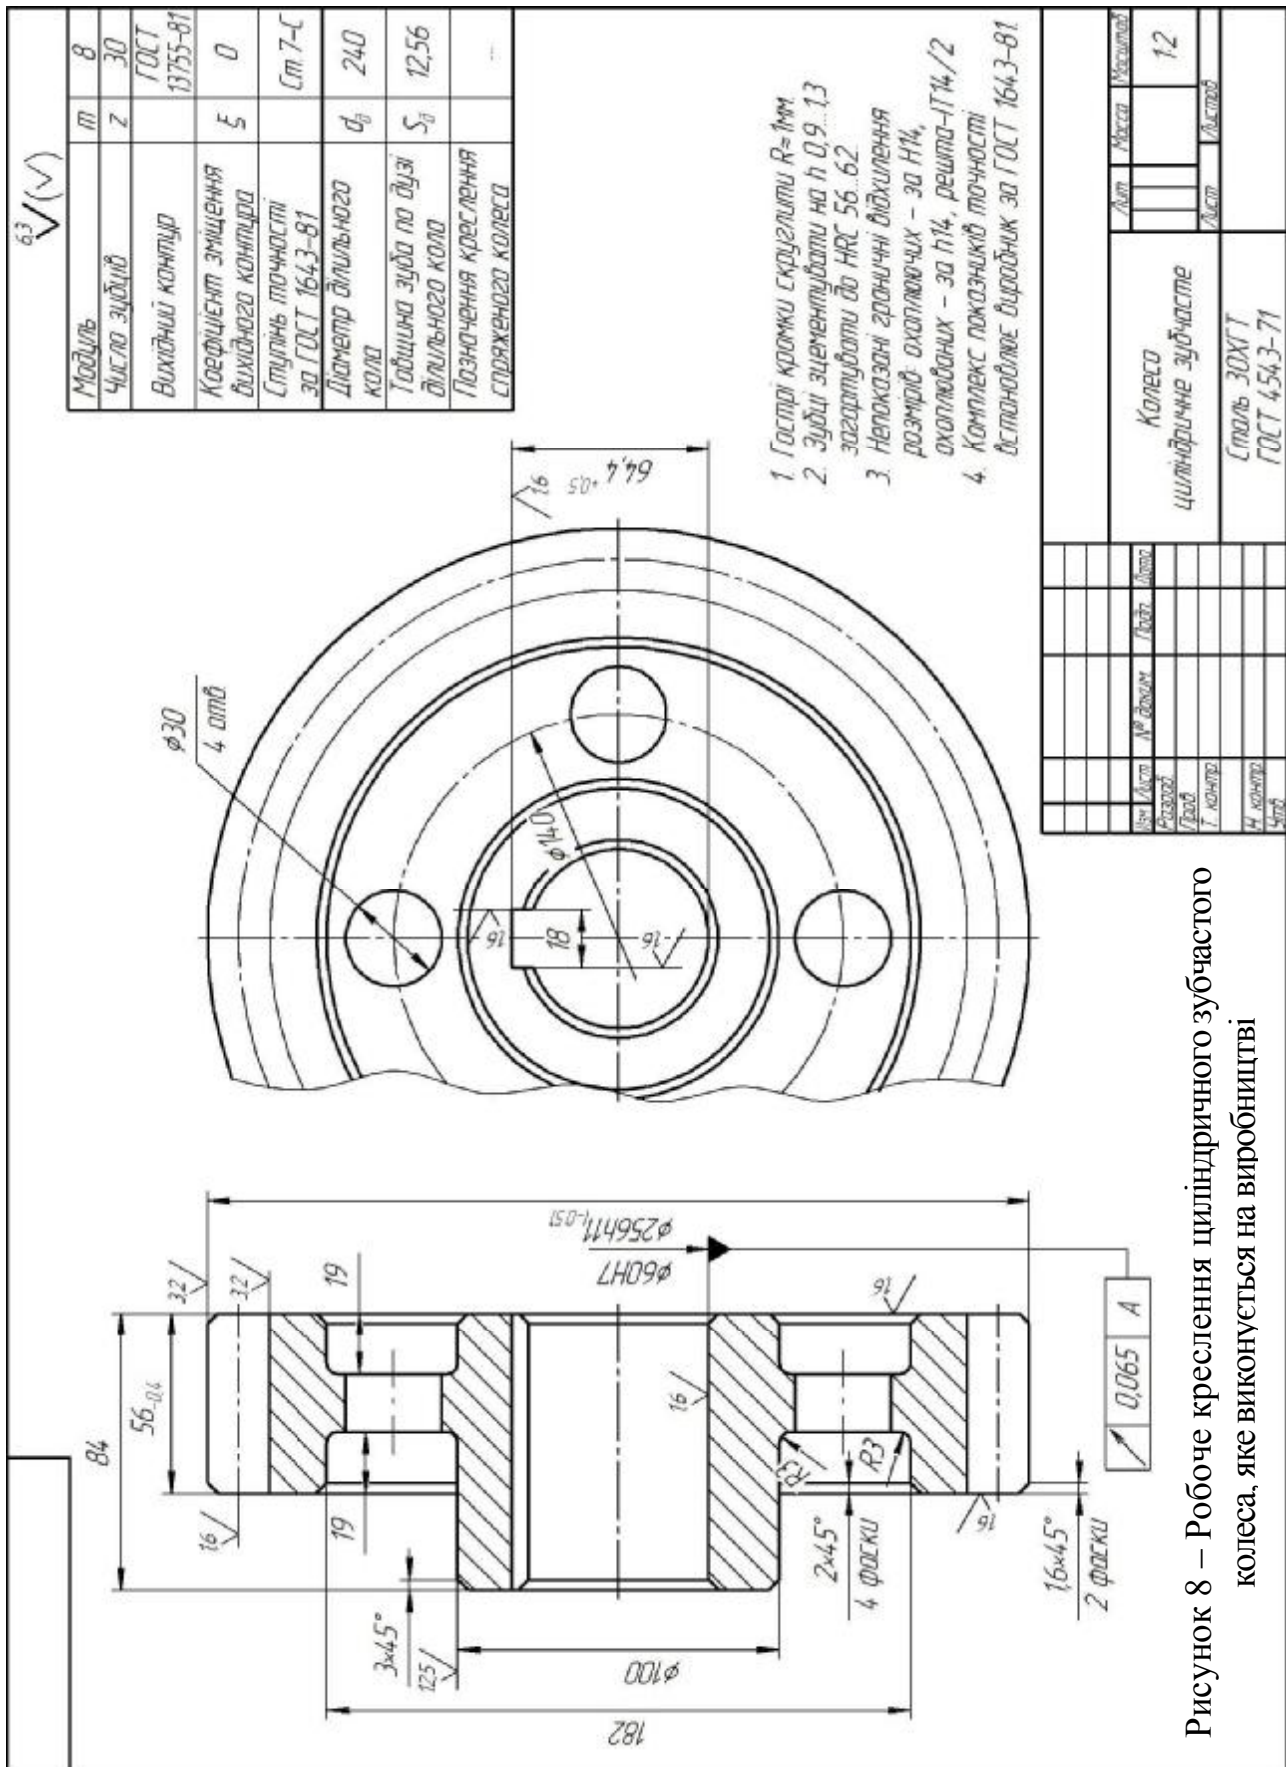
Робоче креслення циліндричного зубчастого колеса, яке виконується на виробництві
